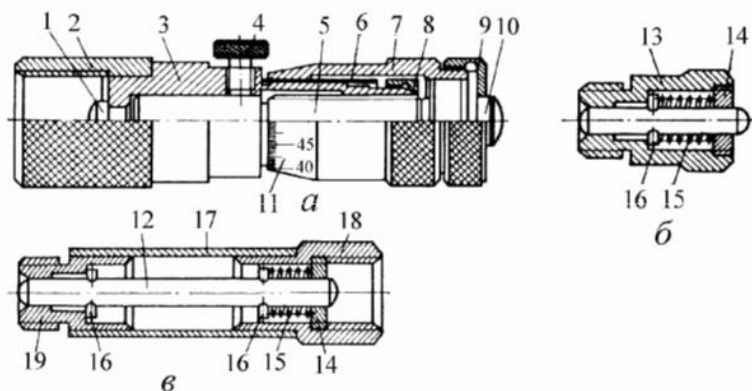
Конструкция микрометрической головки нутромера (а), защитного наконечника (б), удлинителя (в): 1 – измерительный наконечник; 2 – муфта; 3 – стебель; 4 – стопор; 5 – микрометрический винт; 6 – гильза; 7 – барабан; 8 – регулировочная гайка; 9 – затяжная гайка; 10 – микрометрический винт; 11 – круговая шкала; 12 – стержень; 13 – корпус; 14 – гайка; 15 – пружина; 16 – штифт; 17 – трубка; 18 – муфта с внутренней резьбой; 19 – муфта с наружной резьбой.
